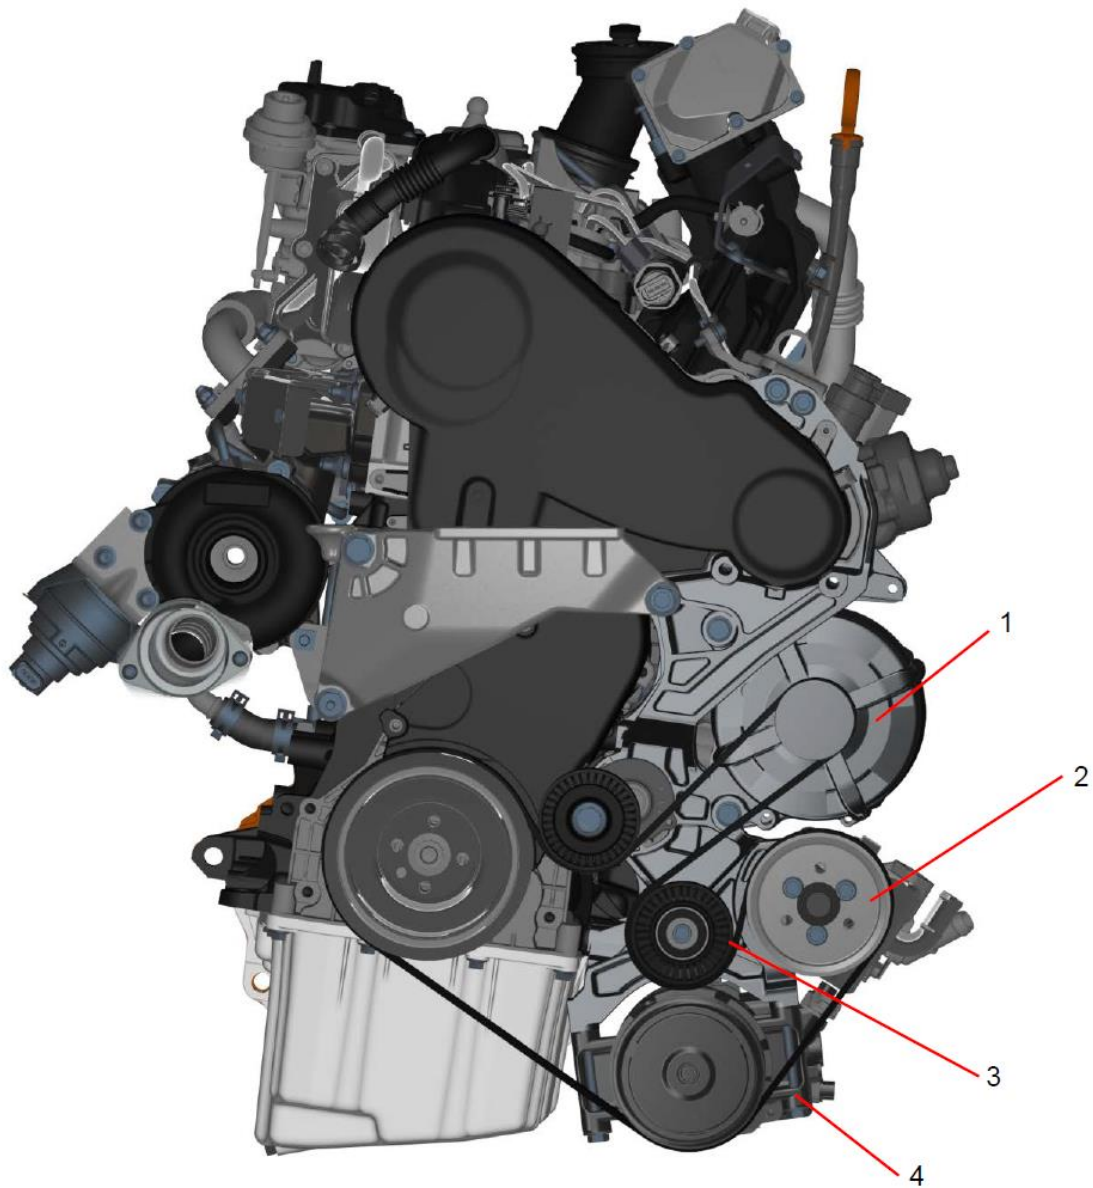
Поликлиновой ременный привод (только схематическое отображение двигателя TDI, фактическое положение двигателя отличается от показанного)
